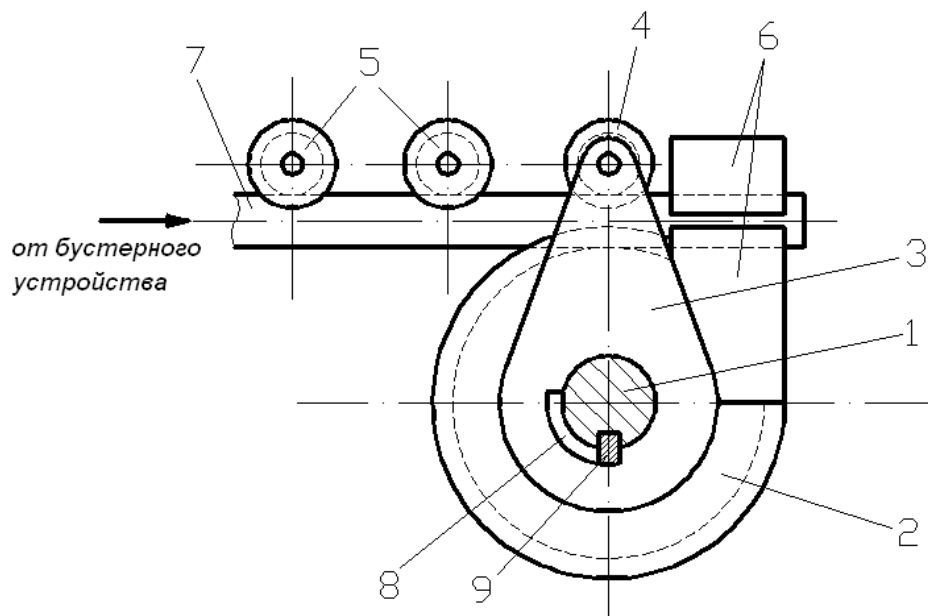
Устройство поворота опорного ролика трубогибочного станка
